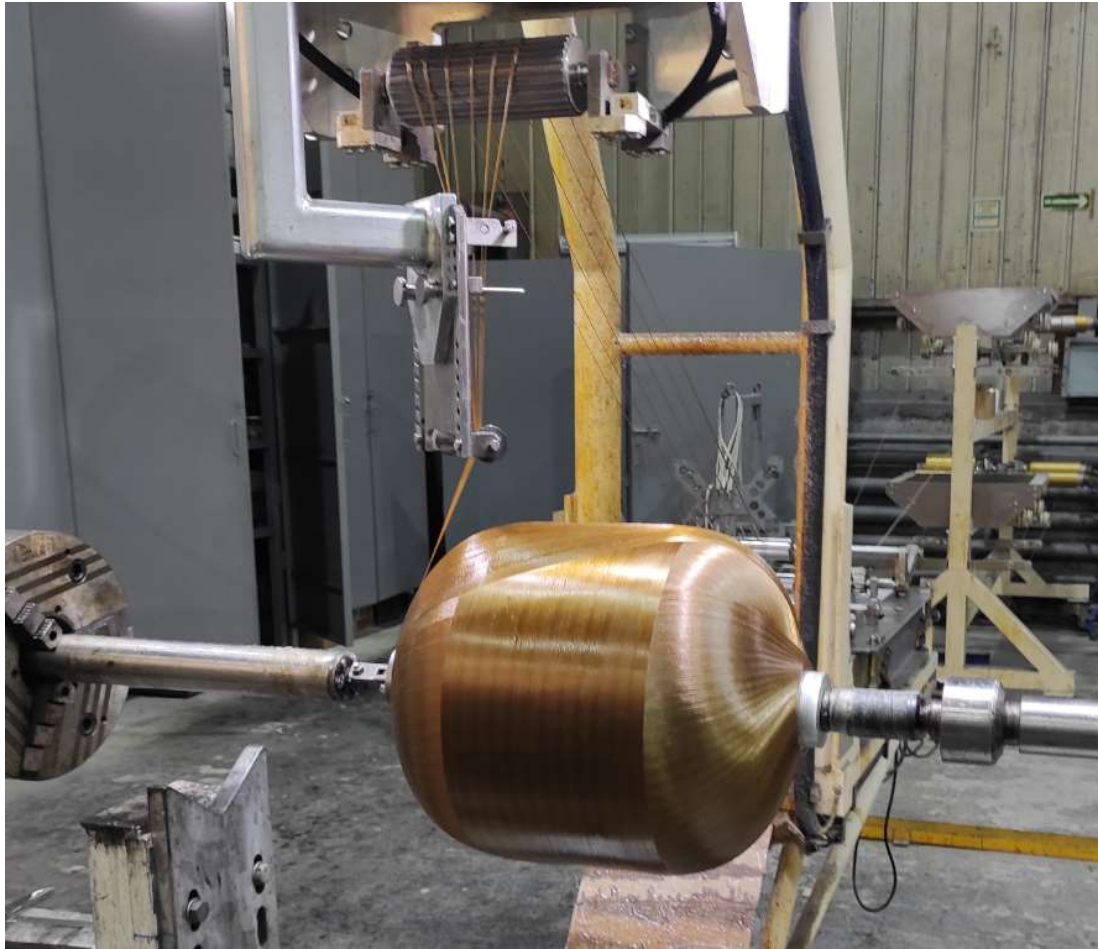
Намотка силового корпуса композитной ёмкости давления
